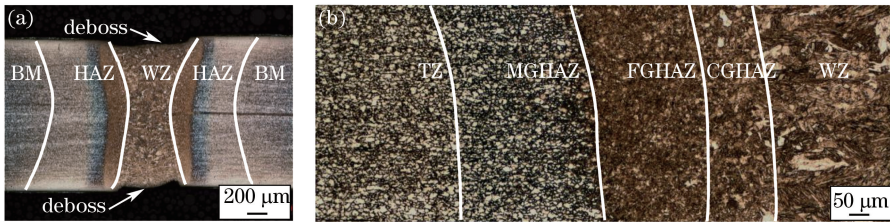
焊接接头宏观形貌。(a) 焊接接头横截面形貌; (b) 焊接接头的区域划分
